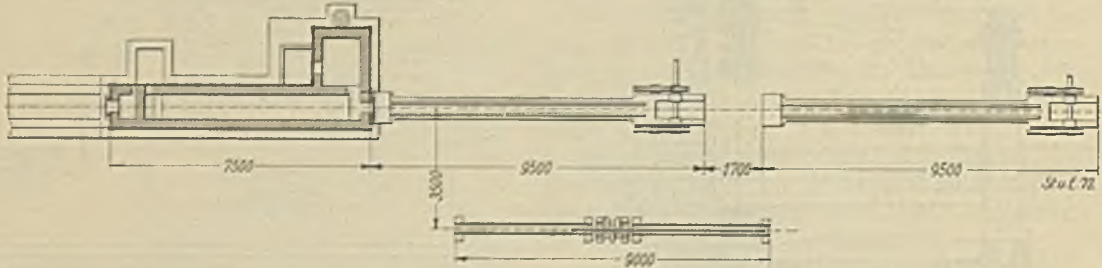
Allgemeine Anordnung einer Schrägwalzen-Richtmaschine mit Bezug auf den Schweißofen, die Zieh- und Kratzbank.
